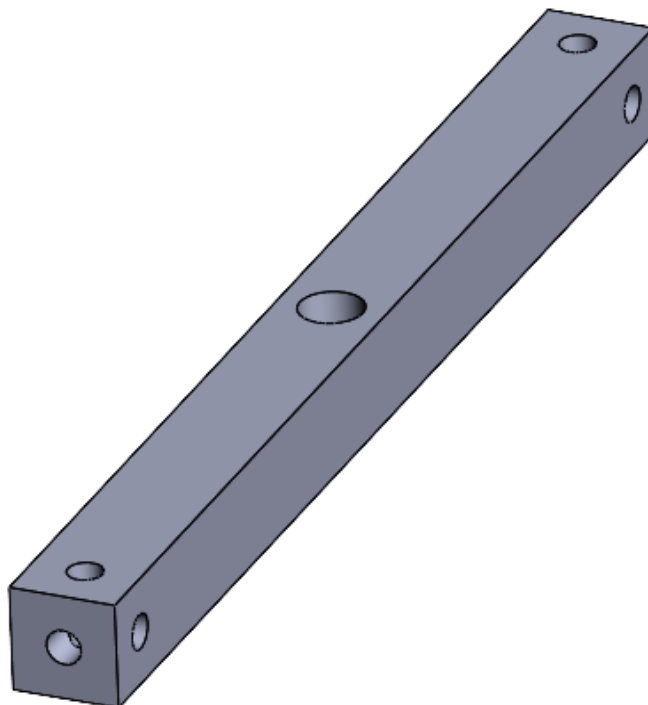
Держатель направляющих передней вертикальной крышки ИТПК
